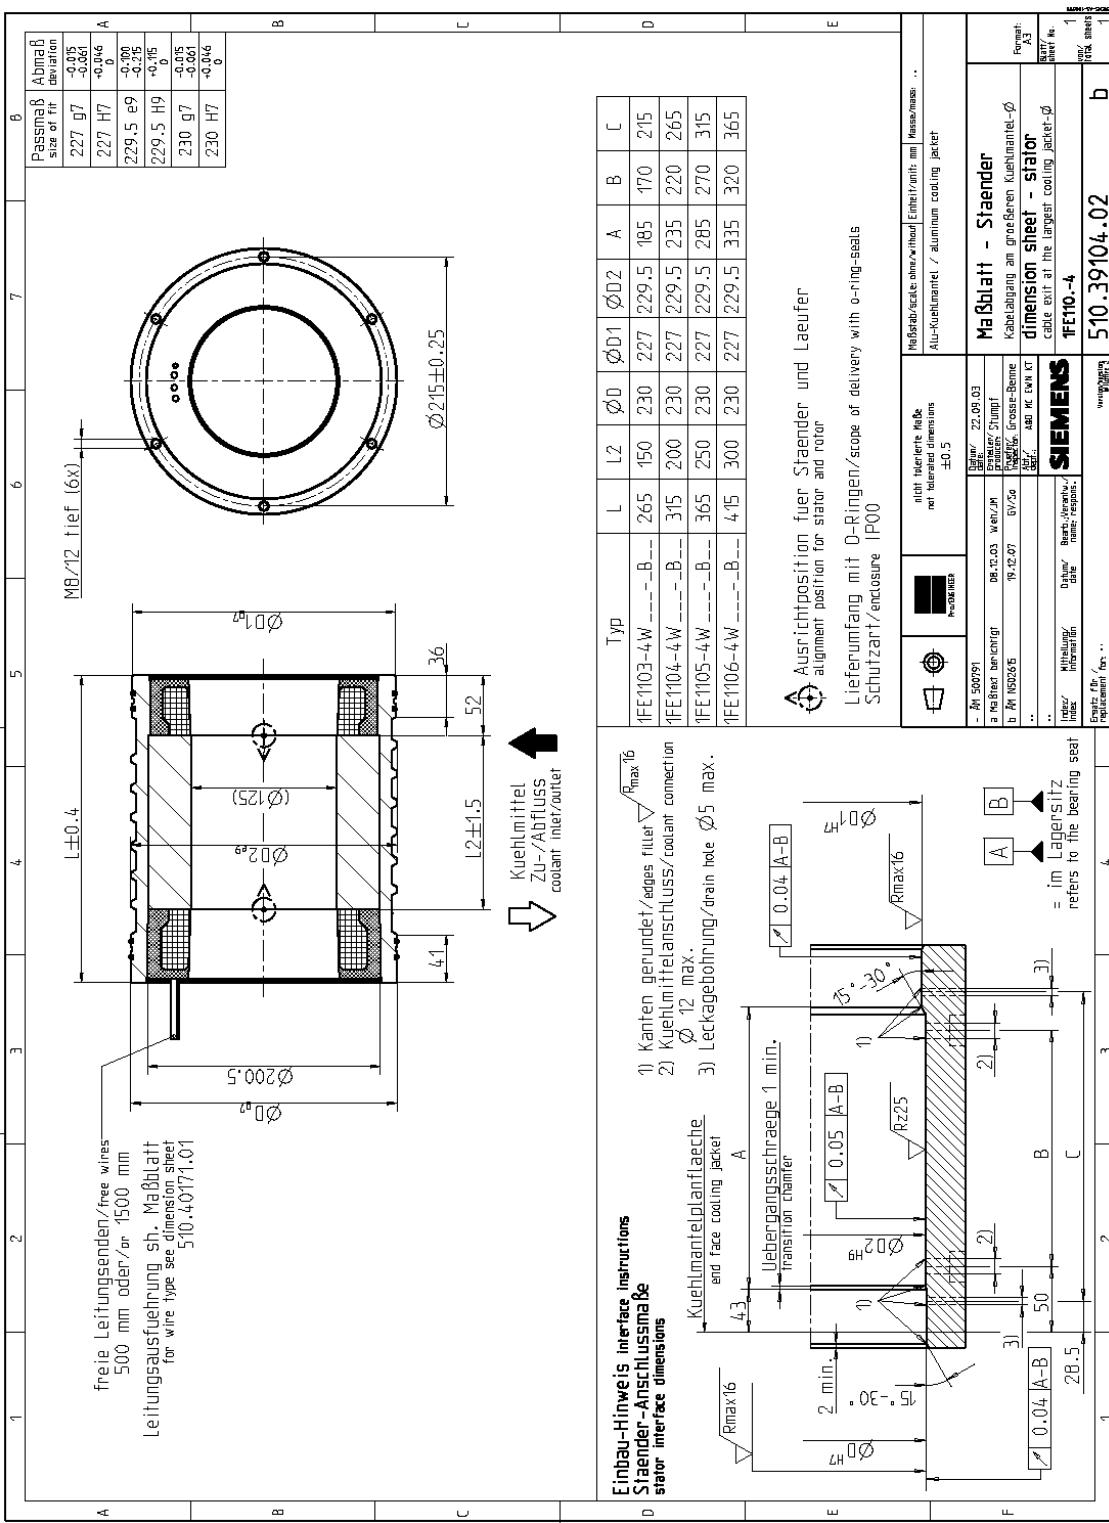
1FE110□-4, Ständer mit Kühlmantel, Kabelabgang am größeren Kühlmanteldurchmesser
